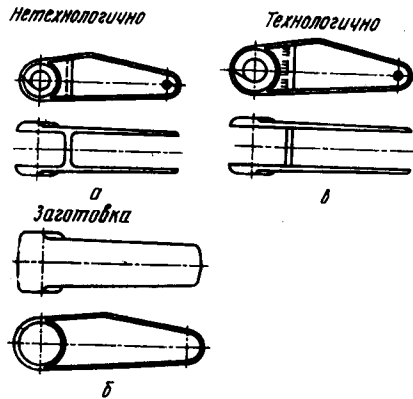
Рычаг (а) из штампованной заготовки (б) и рычаг (в), сваренный из штампованных элементов.
